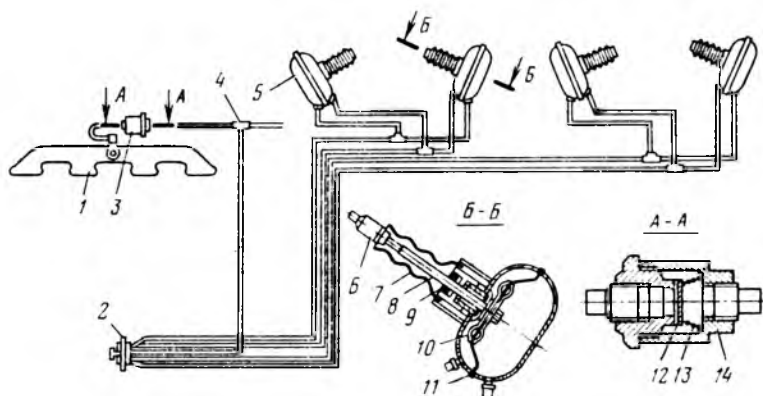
Механизм управления дверьми с вакуумным приводом:
